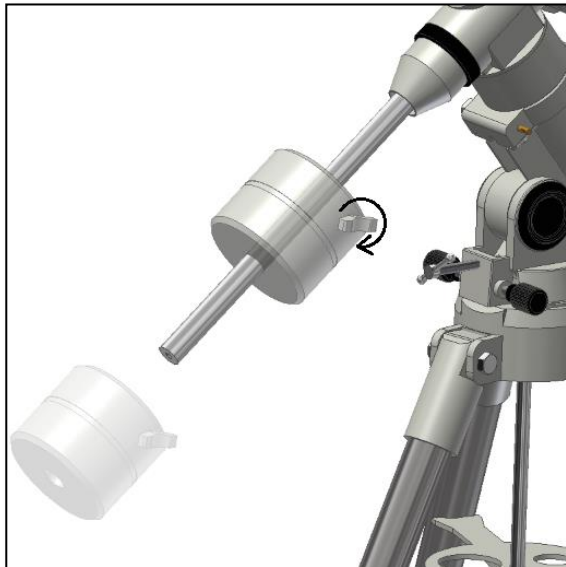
Gegengewicht aufschieben und Sicherungsschraube einschrauben.
